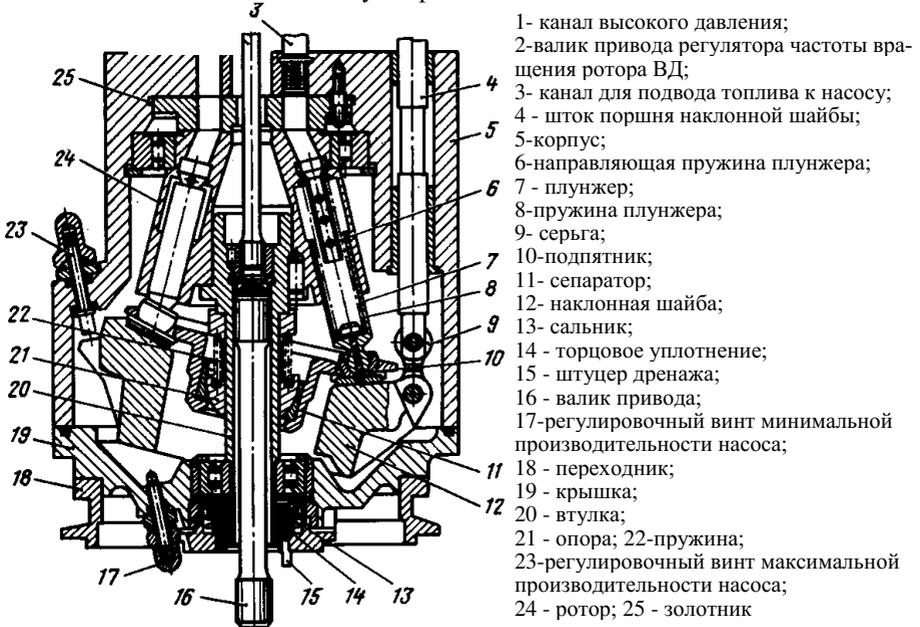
Плунжерный насос высокого давления двигателя Д-30КП [4]
